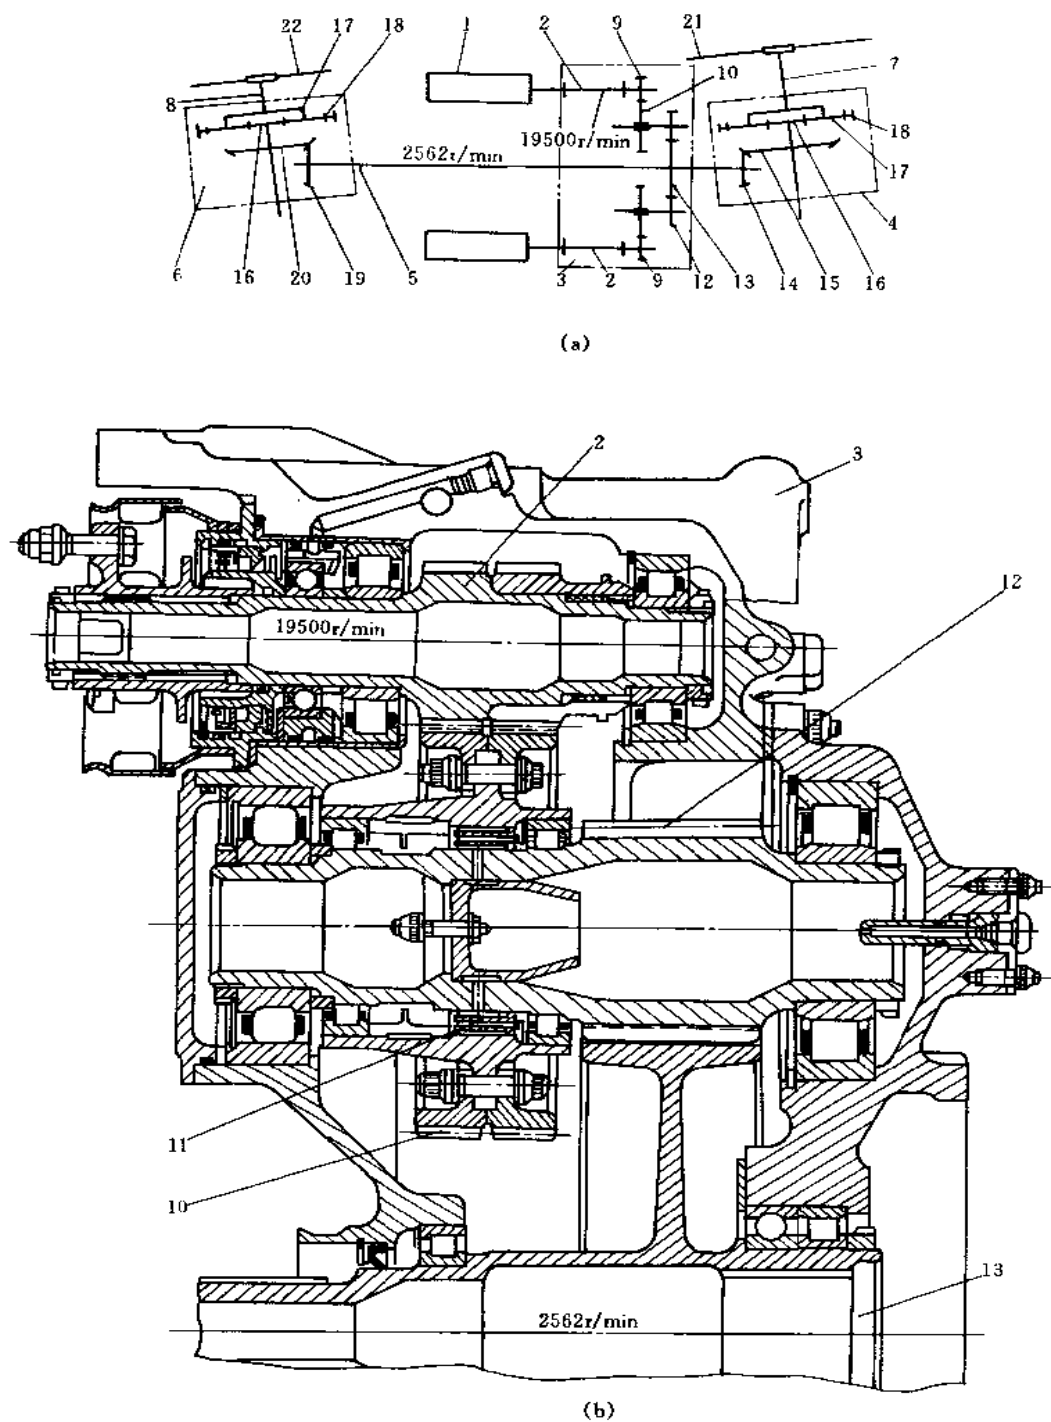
直升飞机的传动装置及空心齿轮轴 (a)、(b)
